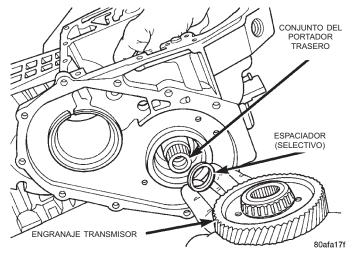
Engranaje transmisor y espaciador (selectivo)
